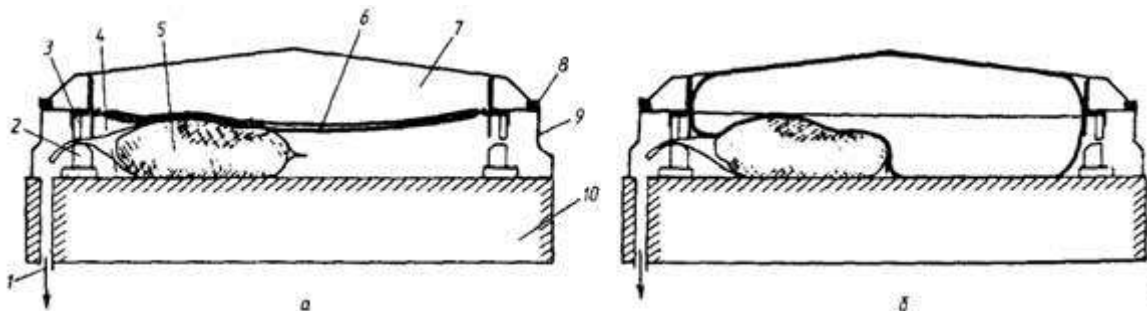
Схема камерної пакувальної машини: а – період завантаження; б – період вакуумування: 1 – патрубок для вакуумування; 2 – зварювальна губка, 3 – затискачі, 4 – пакет; 5 – продукт, 6 – мембрана; 7 – кришка, 8 – ущільнення; 9 – камера; 10 – корпус
